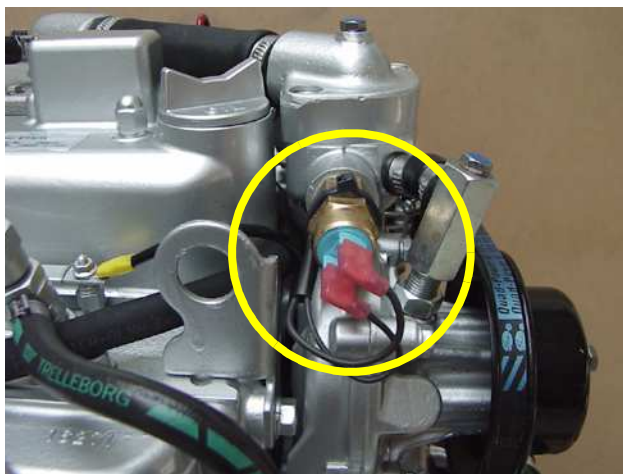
Thermoschalter am Thermostatgehäuse
